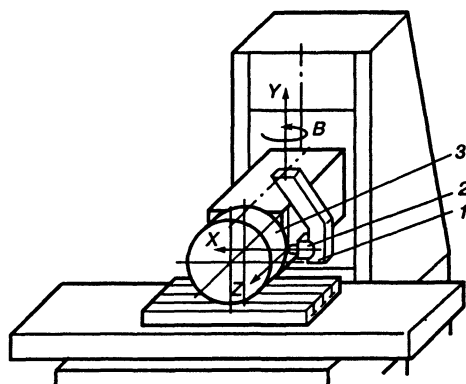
Механизм правки станка ЗЕ711ВФ3—1 с ЧПУ
